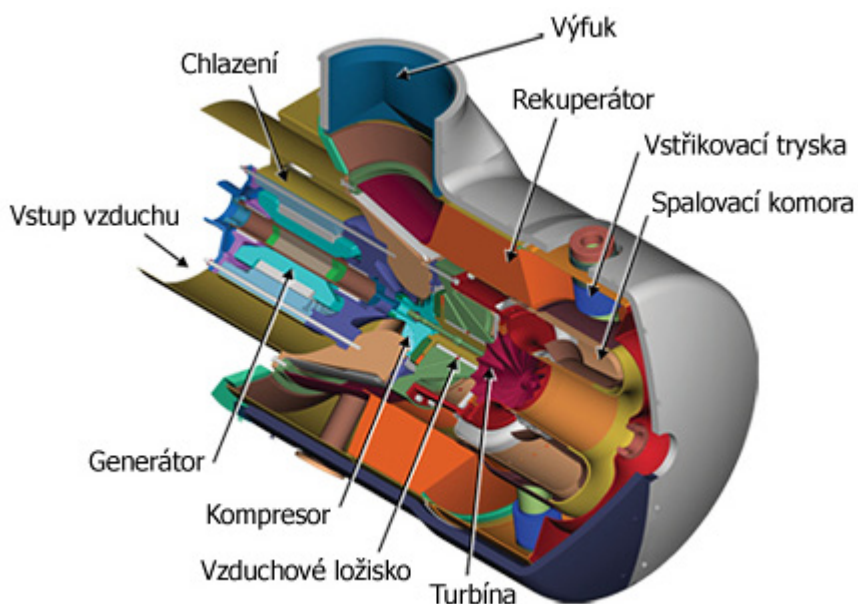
Společný rotor kompresoru a turbíny [15]
